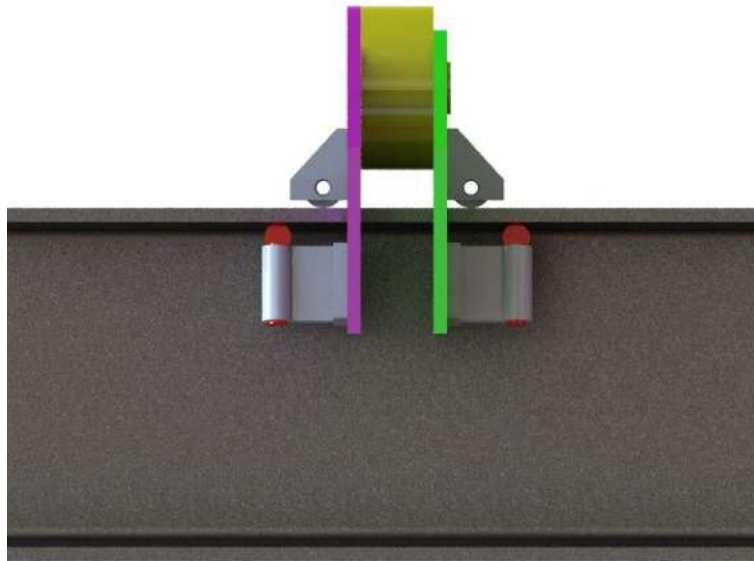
Vista lateral del soporte guía con elementos rodantes.
